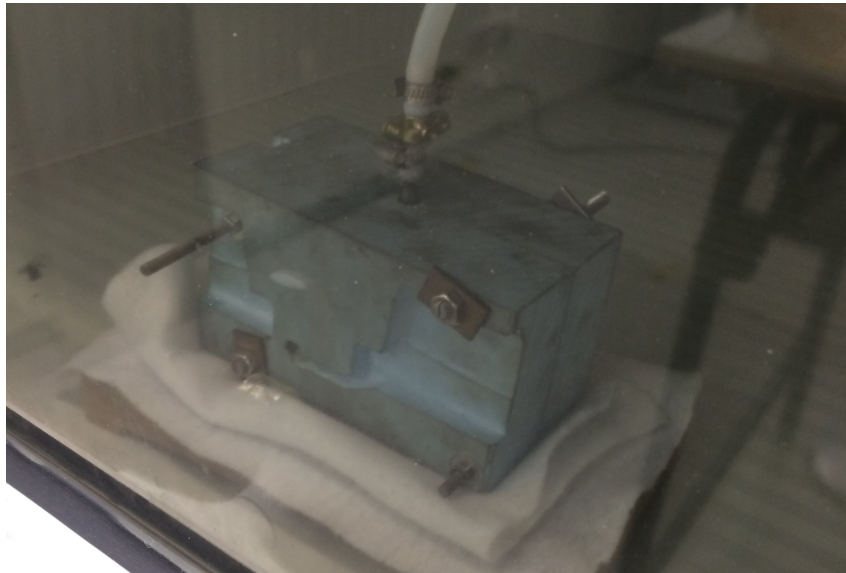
Fabricación I. Colocación de la bolsa en la parte externa del molde. (Fuente: Propia)
